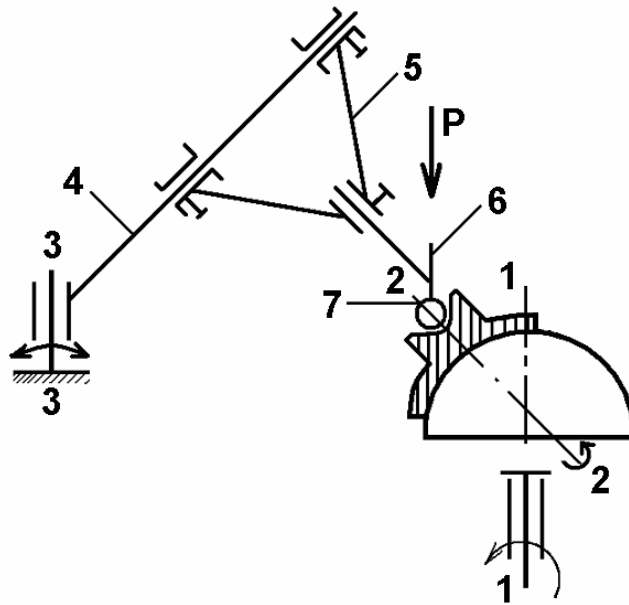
Кінематична схема роботи верстата типу ШП
